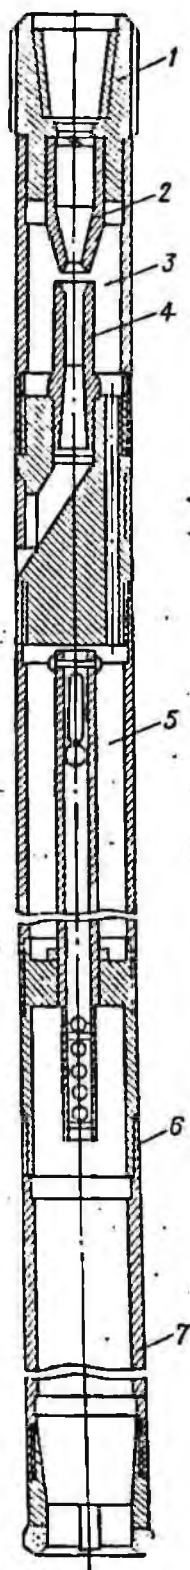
Одинарный эжекторный колонковый снаряд типа ОЭС-73 конструкции ЦНИГРИ.
